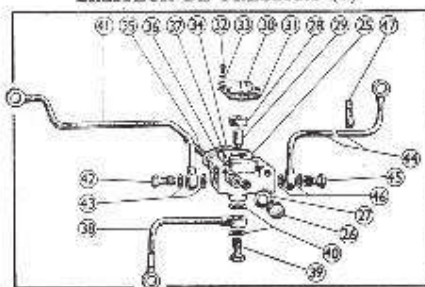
SCHEMA DE GRAISSAGE DU P6.
